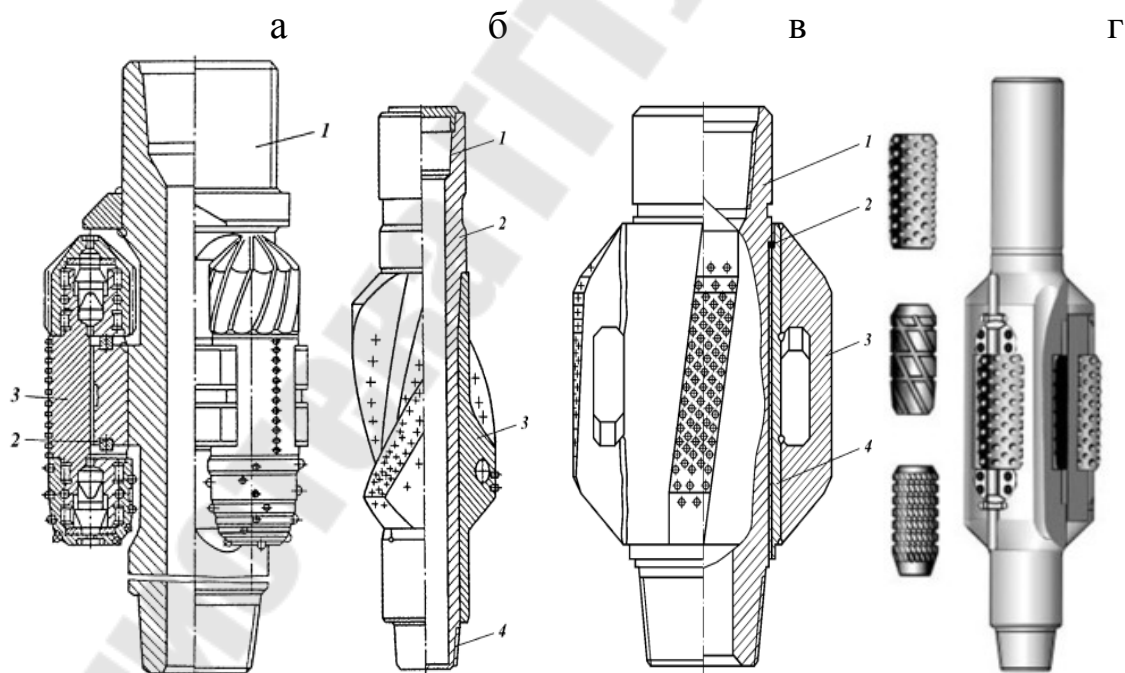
Конструкции опорно-центрирующих устройств: а – калибратор шарошечный типа КШУ; б – калибратор со сменными спиральными лопастями типа 8 КС; в – калибратор – центратор с прямыми лопастями типа КЦЛ; г – стабилизатор со сменными шарошками
